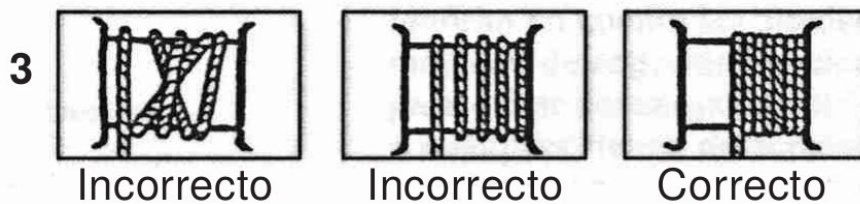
Enrollado del cable: incorrecto / incorrecto / correcto
